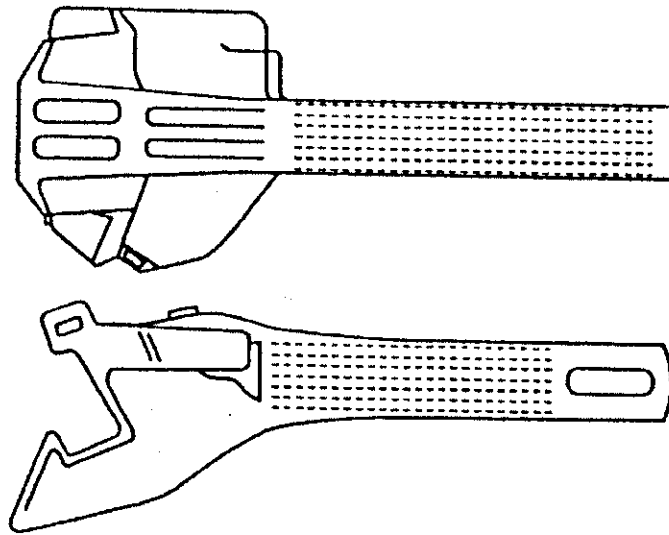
Контроль хвостовика корпуса автосцепки
